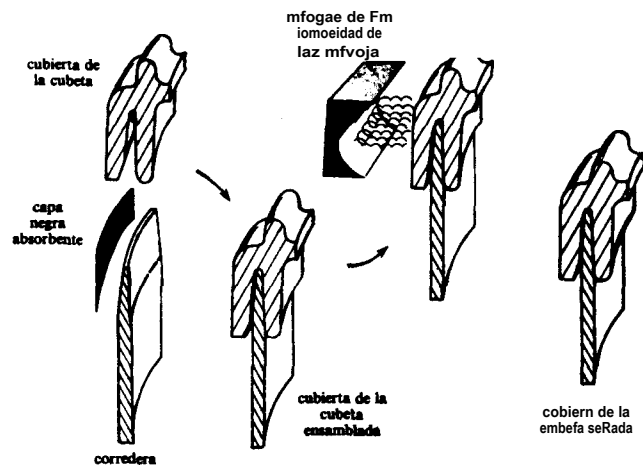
Ensamblaje de la cubierta sellada de la cubeta y secuencia de sellado (esquemático).
